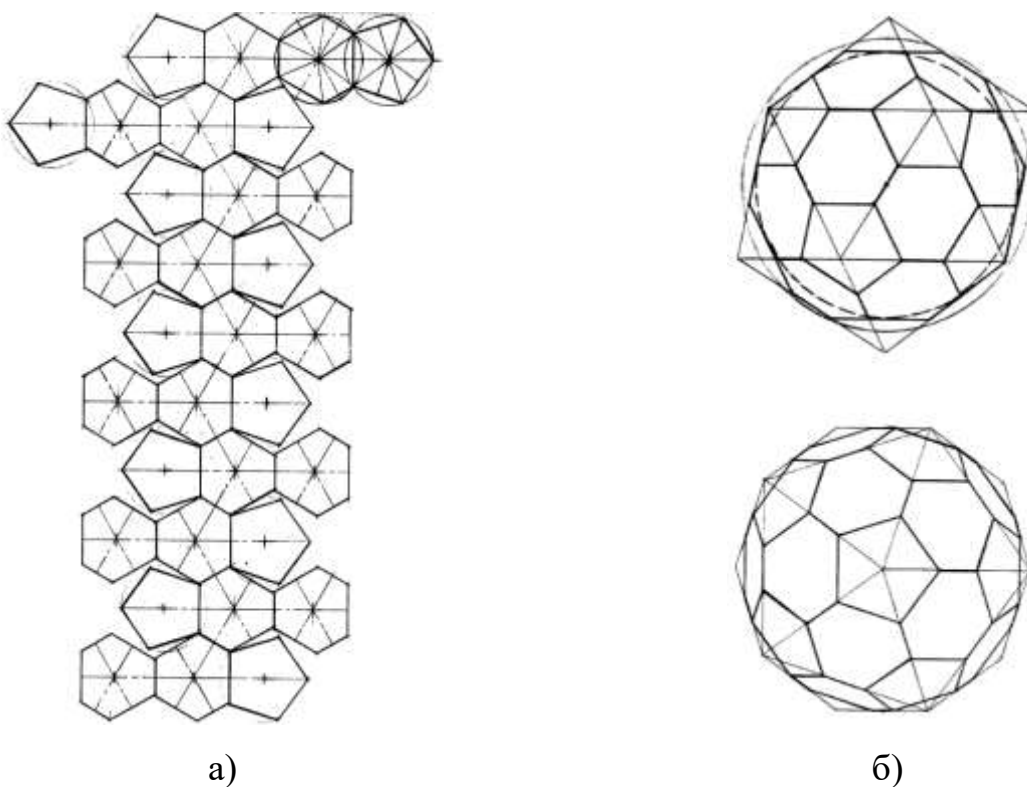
Виготовлення сфери за допомогою ікосаедра: а- заготовка, б- зібрана сфера [9]
